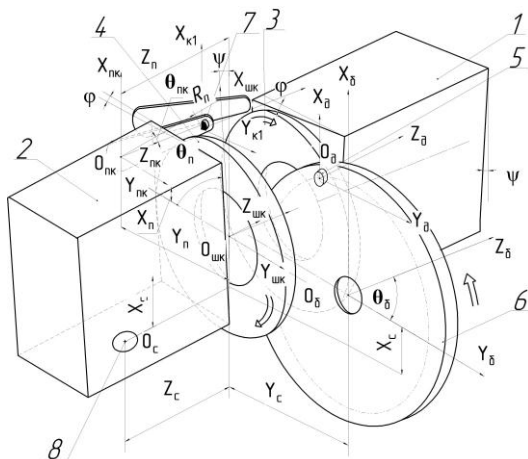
Розрахункова схема формоутворення торців хрестовин карданних валів
